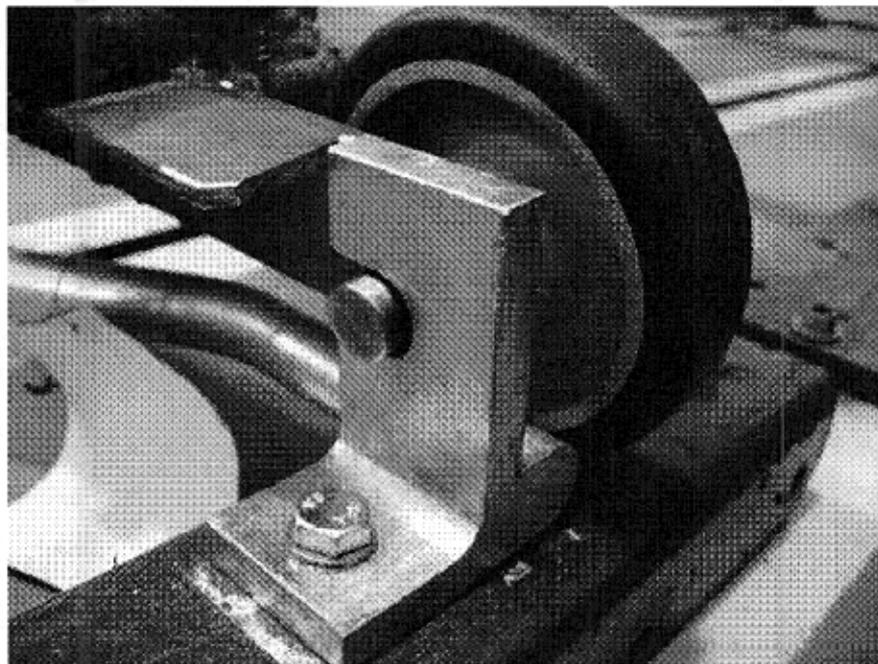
Lado esquerdo da amostra 2 após ensaio.
